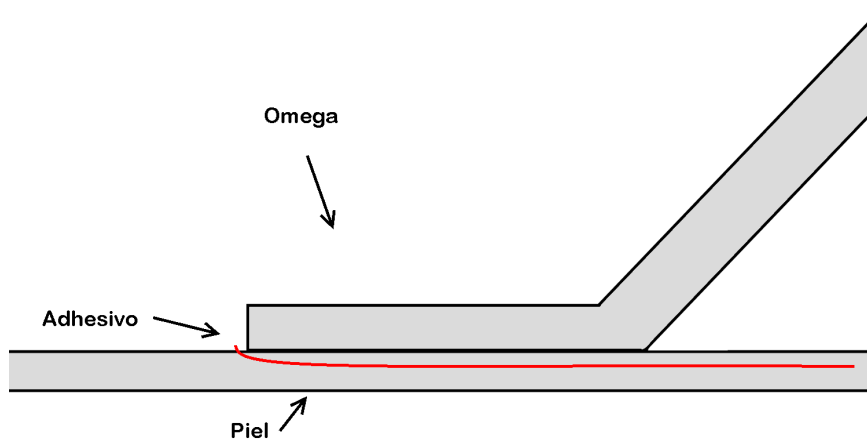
Detalle de grieta inicial en F-F2
